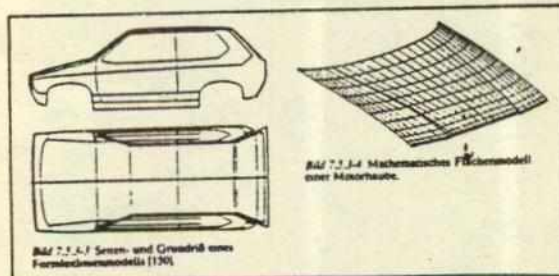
Seiten- und Grundriss eines Formteilmodells (130)
